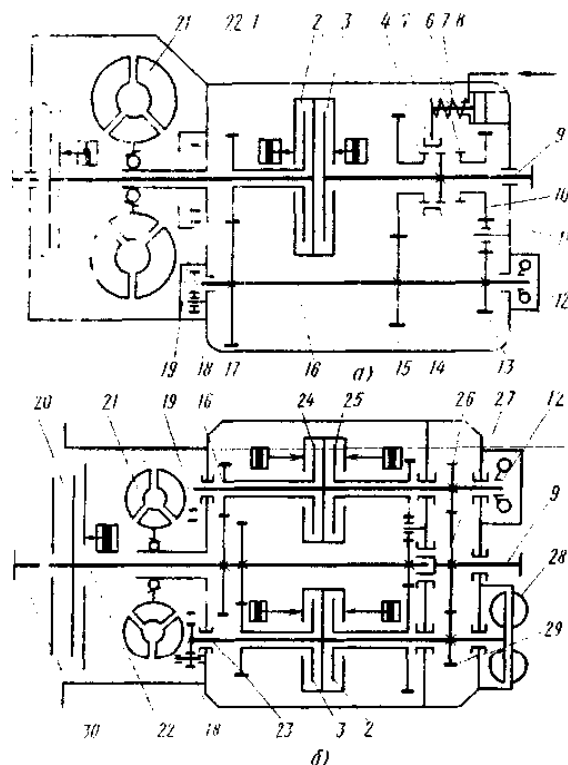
Схемы гидромеханических коробок передач: а – двухступенчатой; б – трехступенчатой.
